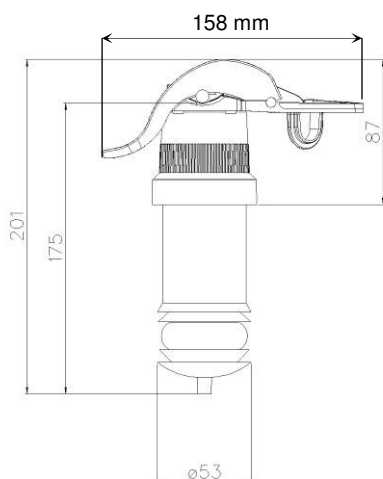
LINETROLL 110Eμr/110Eμr dimensiuni fizice. Toate dimensiunile in mm.
